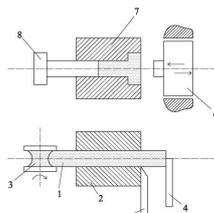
Схема высадки на холодновывсадочном автомате: 1 – заготовка; 2 –отрезная матрица; 3 – ролик подачи; 4 – регулируемый упор; 5 – отрезной нож; 6 – высадочный пуансон; 7 – высадочная матрица; 8 – ползун
